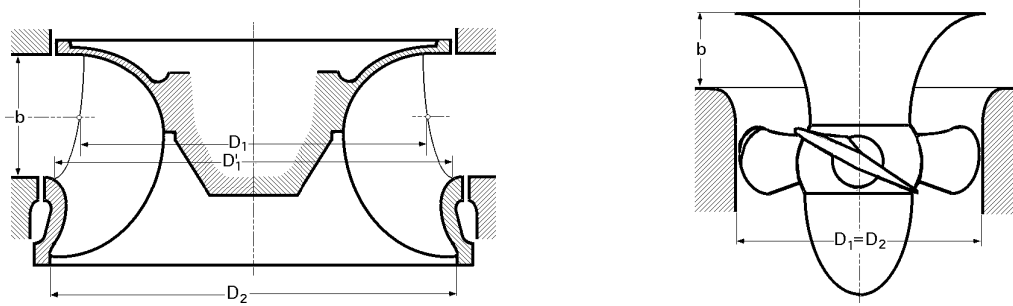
Dimensiones de rodets Francis y Kaplan
